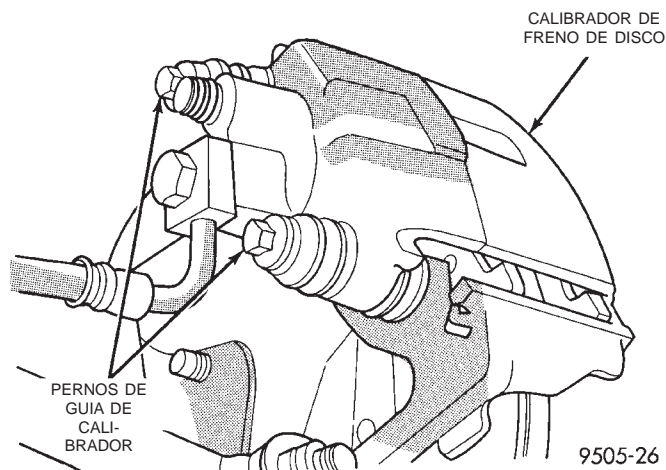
Pernos del pasador guía del conjunto de calibrador
